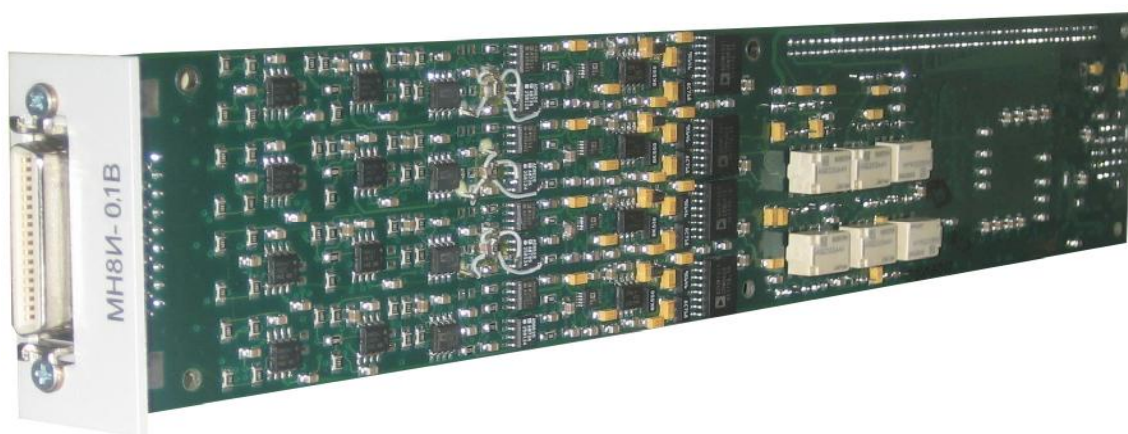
Внешний вид измерителя MN8И-0,1В ФТКС.468266.023-02
